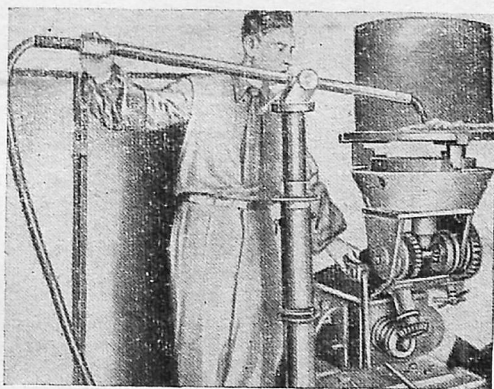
Сварка под слоем флюса наружного кольцевого шва.
